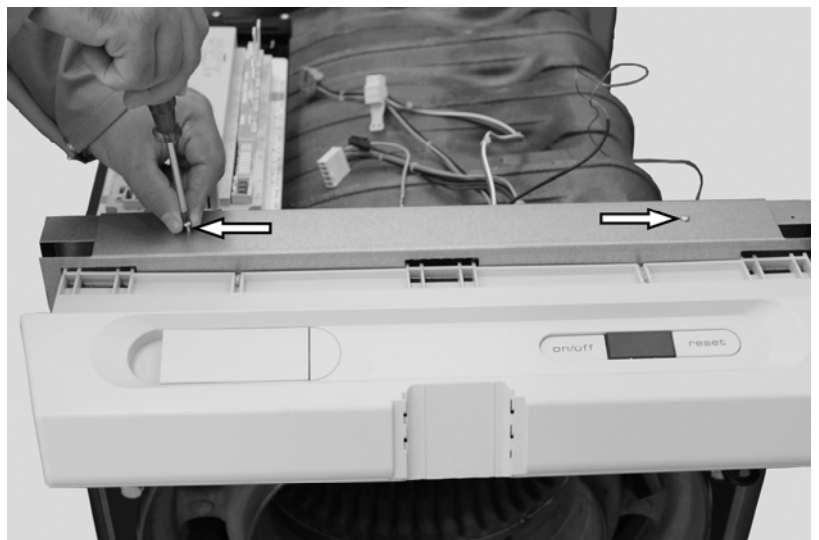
Das Kesselschaltfeld mit zwei Blechschrauben befestigen.
